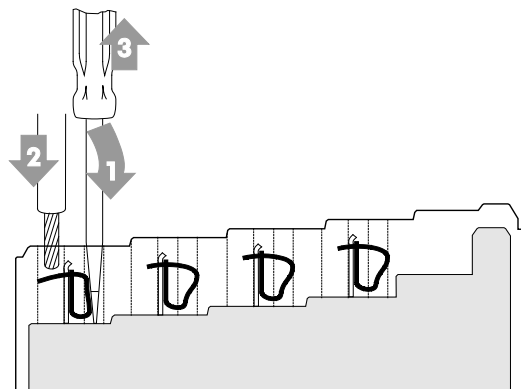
Leiter an CAGE CLAMP® anschließen
